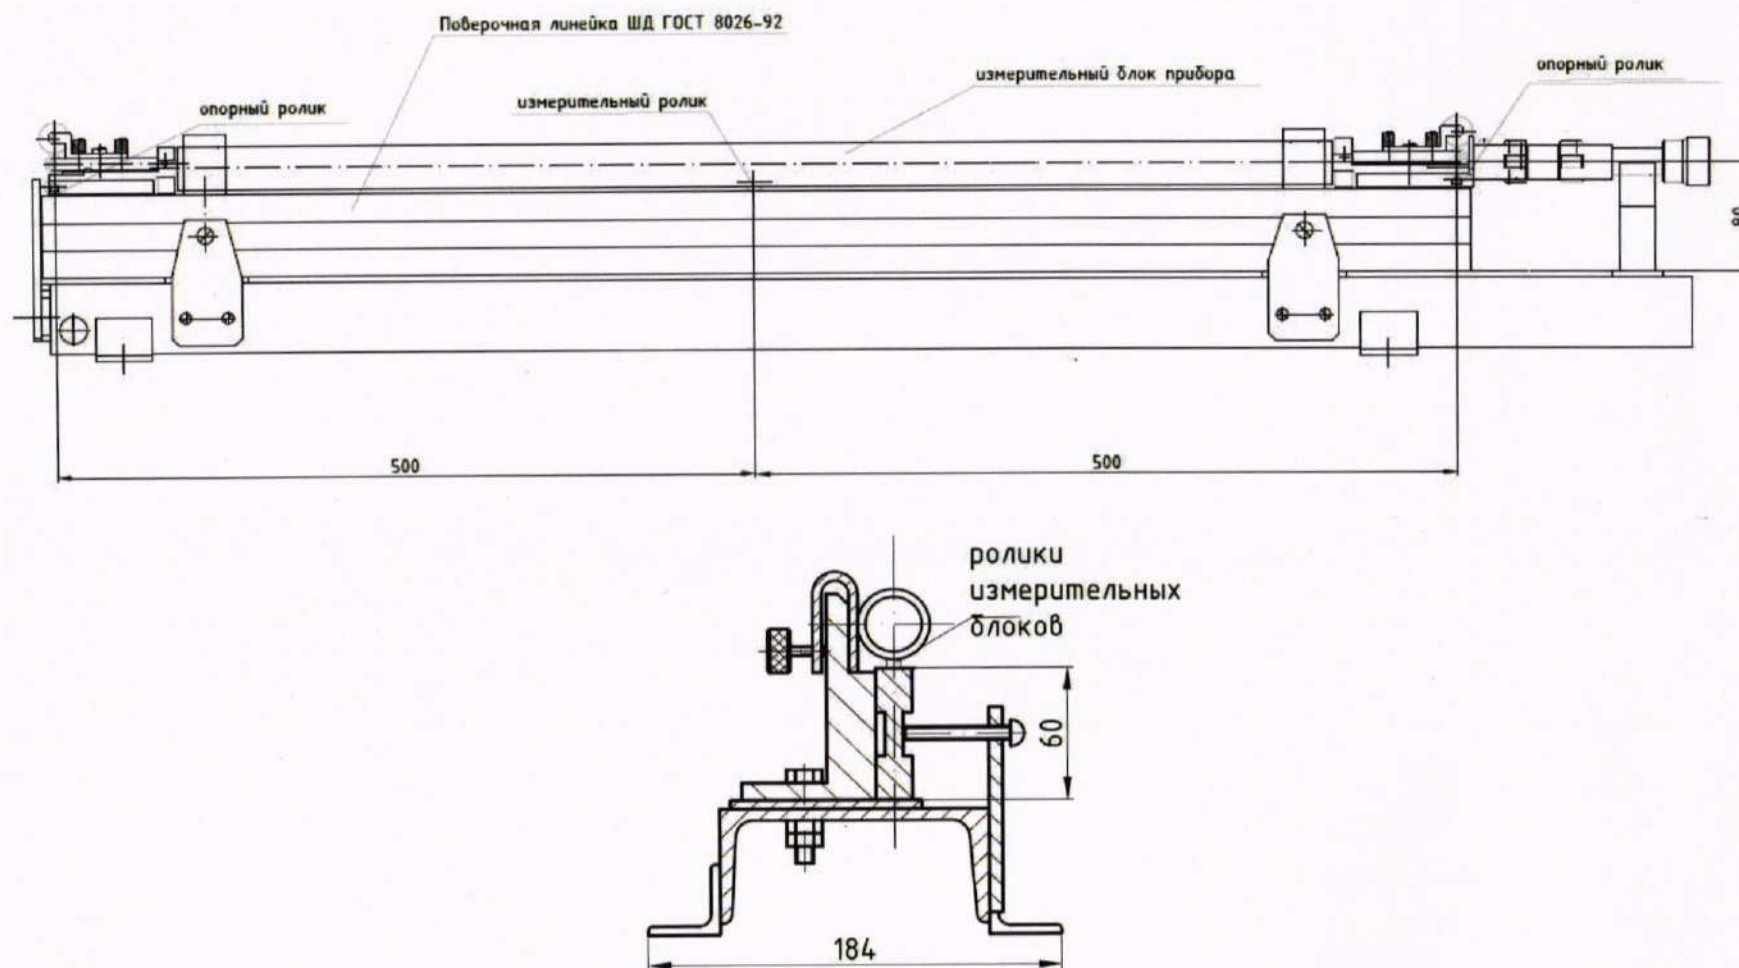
Приспособление поверочное ПИКА-АС1М6-40-122.06.000
